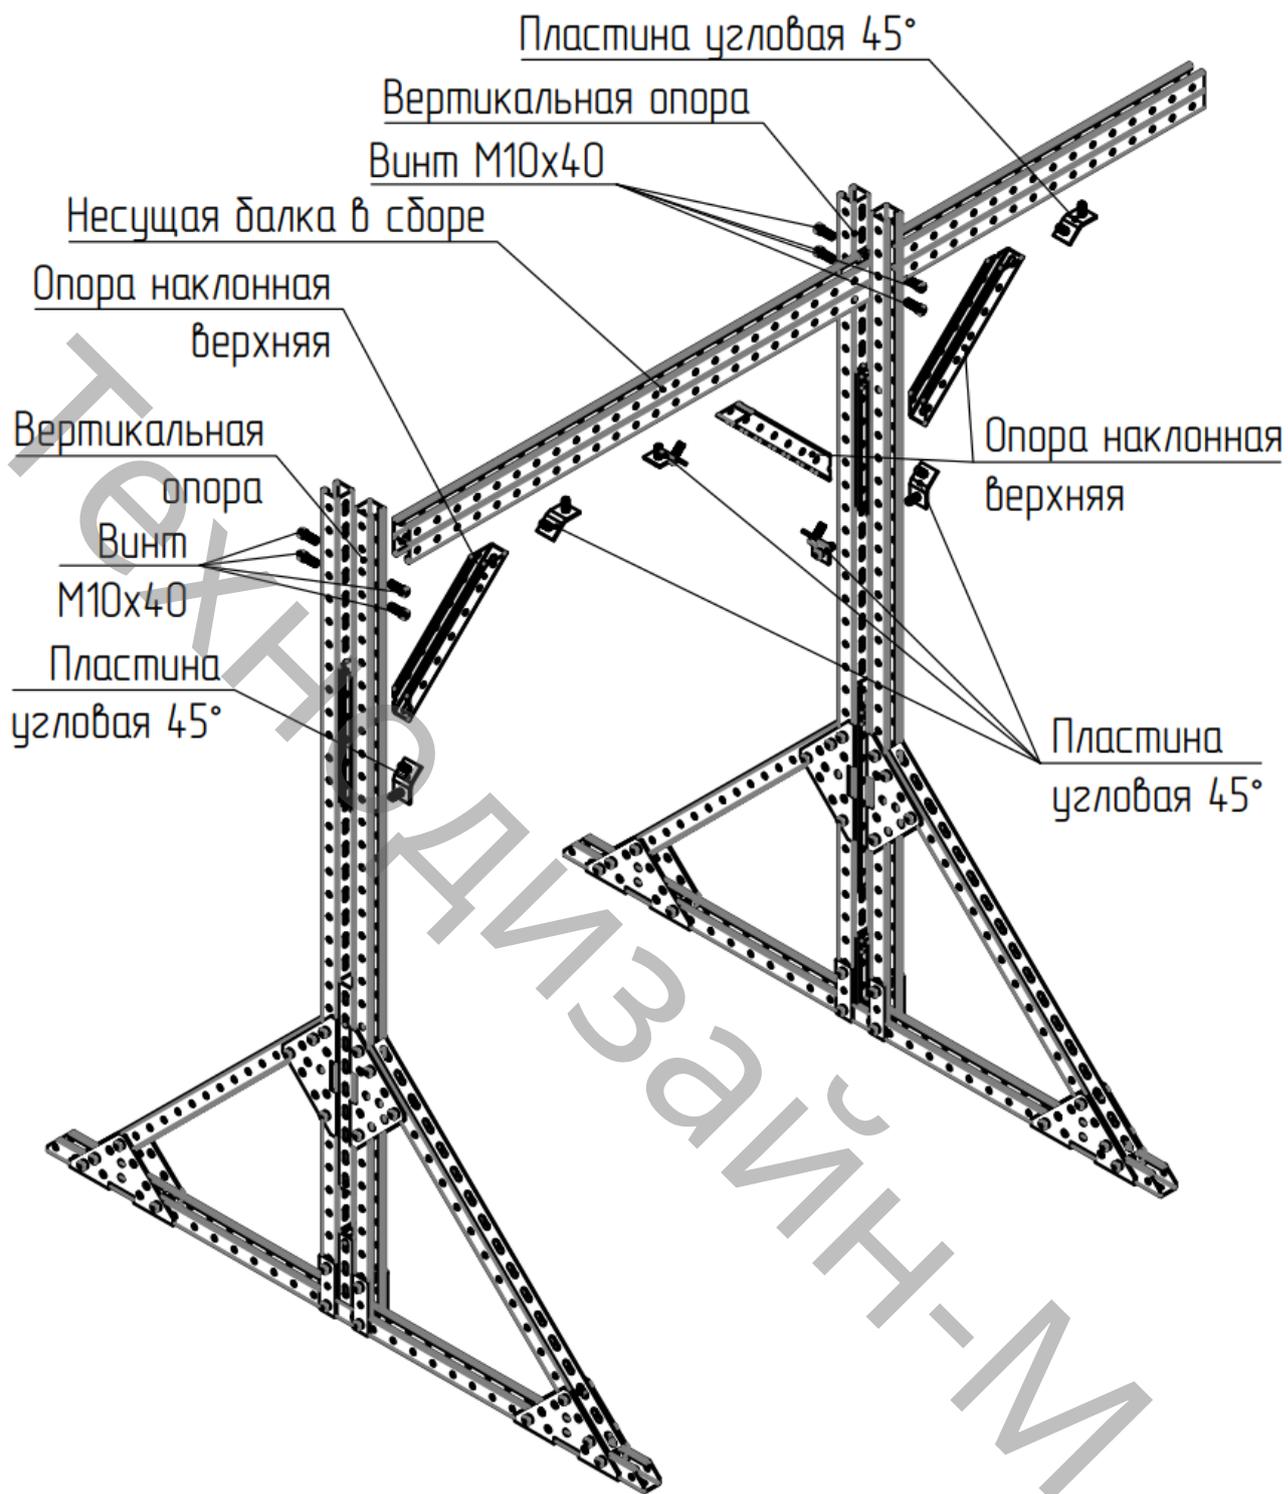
Схема установки несущей балки. СПМ, исполнение 2.
